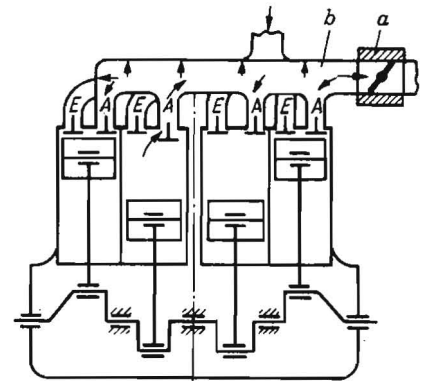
Motor mit abgasdrosselnder Motorbremse:
